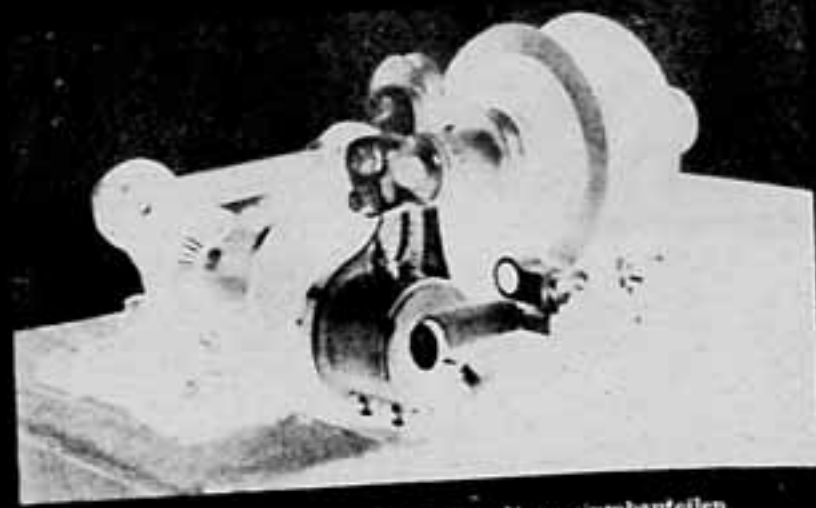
Zigarettenmaschine mit Magnesiumbauteilen.
